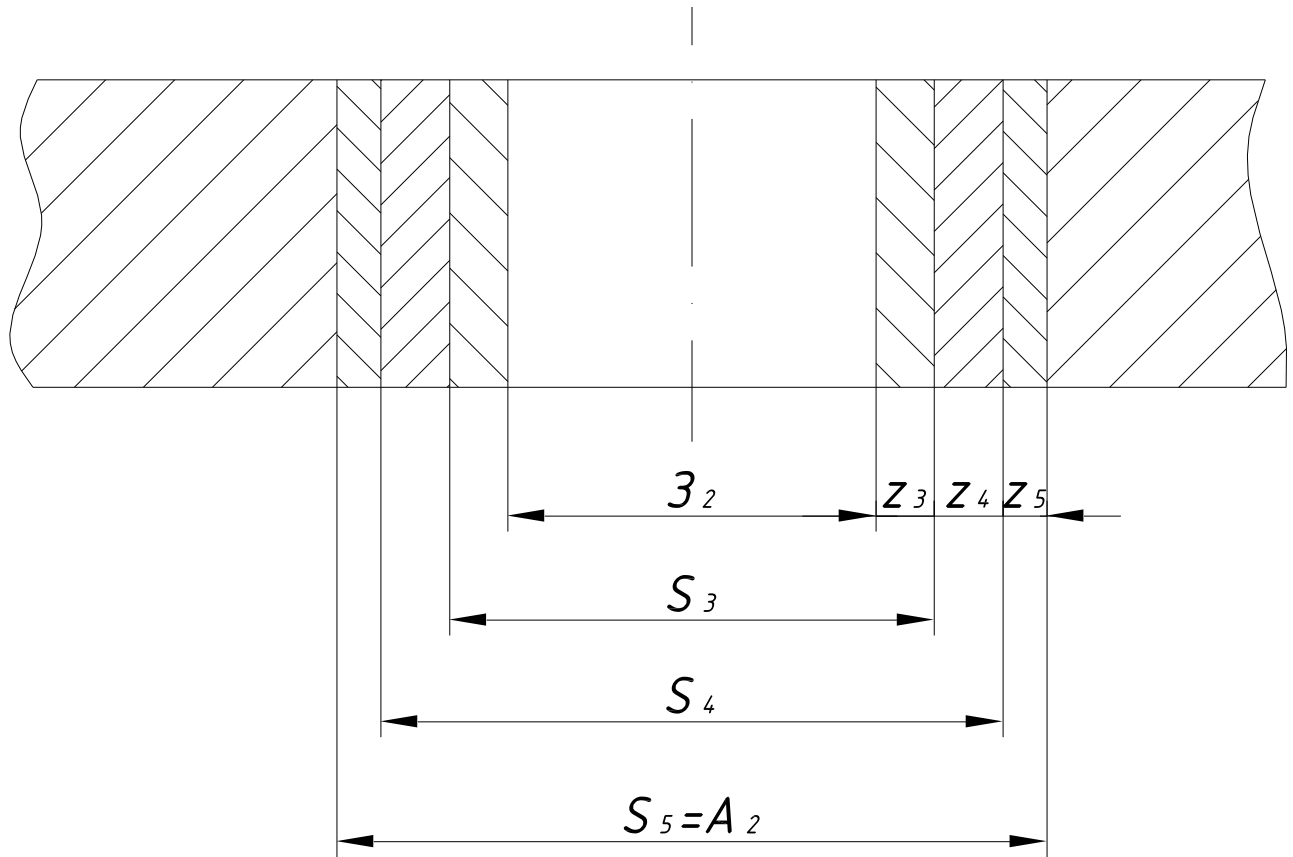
Схема для розрахунку розмірного ланцюга
